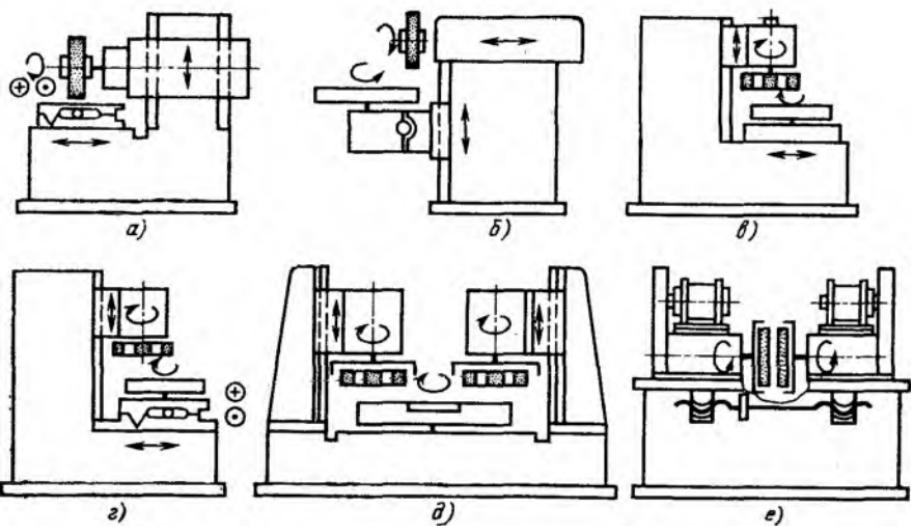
Схемы плоскошлифовальных станков (с обозначением их движения) с горизонтальными шпинделями, работающими периферией шлифовального круга, с прямоугольным (а) и круглым (б) столом; с вертикальными шпинделями, одношпиндельные, работающие торцом шлифовального круга, с прямоугольным (в) и круглым (г) столом; двухшпиндельные станки, работающие торцом шлифовального круга с двумя вертикальными (д) и двумя горизонтальными (е) шпинделями
